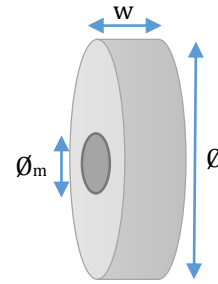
Dimensiones de la probeta y del disco para el ensayo de desgaste.
